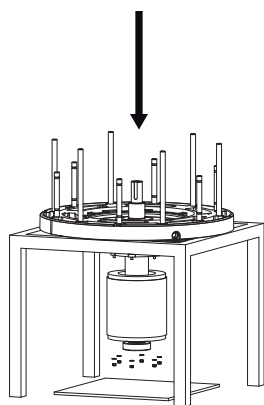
Dépose de l'ensemble rotor (J 604)
